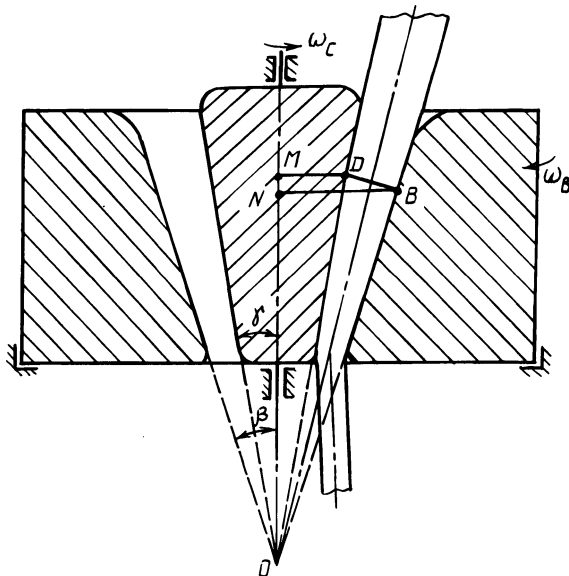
Схема волочения заготовки с перекатыванием через кольцевой зазор
